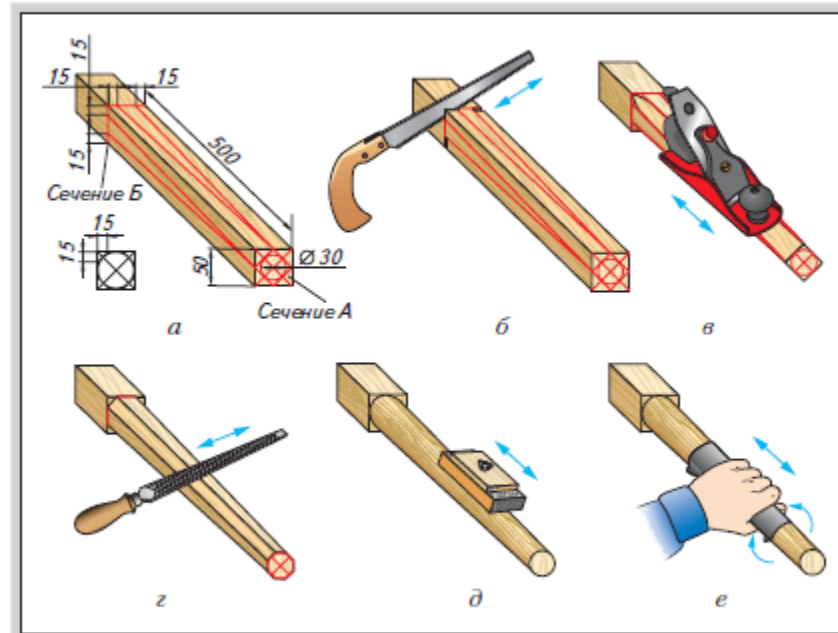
Технология получения конической формы детали ручным инструментом (на примере ножки стола): а – разметка; б – запиливание; в – строгание рубанком; г – зачистка напильником; д – обработка шлифовальной колодкой; е – полировка шлифовальной шкуркой
